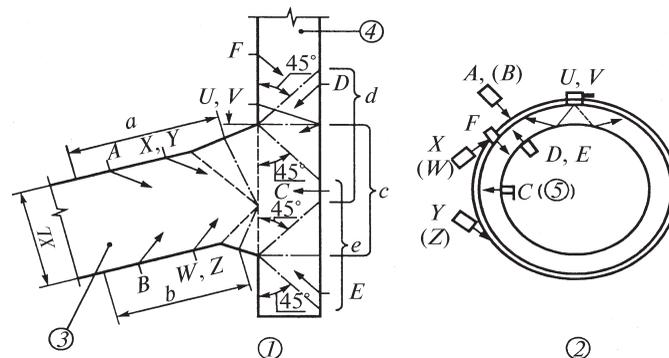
Сварное соединение патрубка (насадное):
